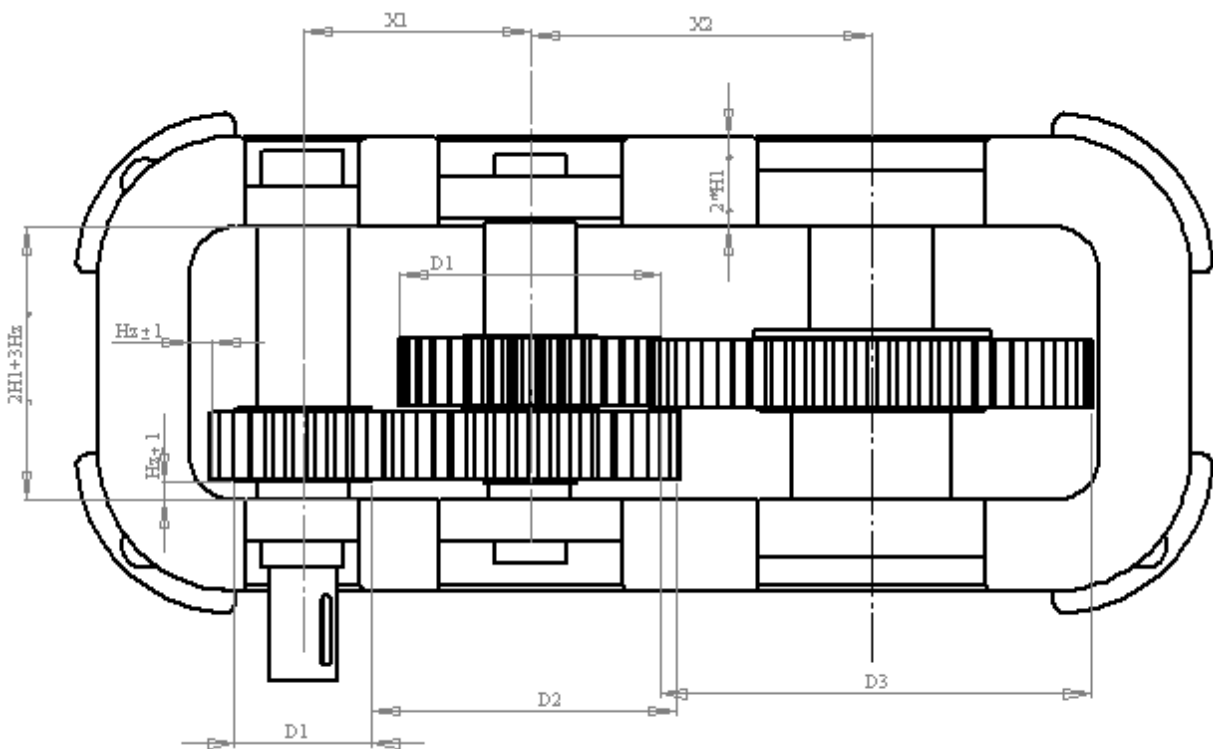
Эскиз редуктора, вид сверху, крышка условно не показана
